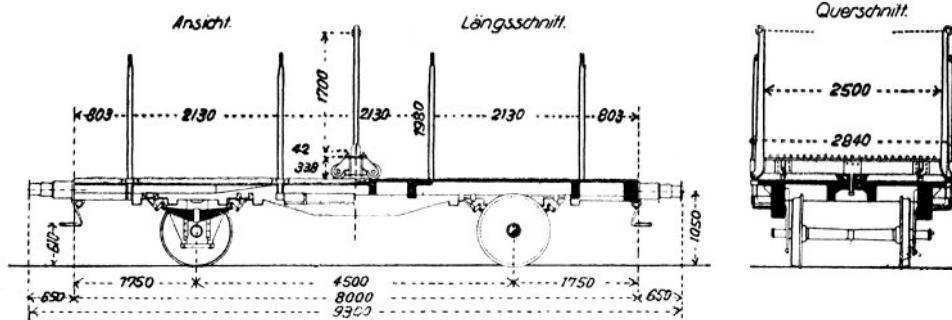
Holzwagen aus Eisenbeton für 15 t Ladegewicht.
